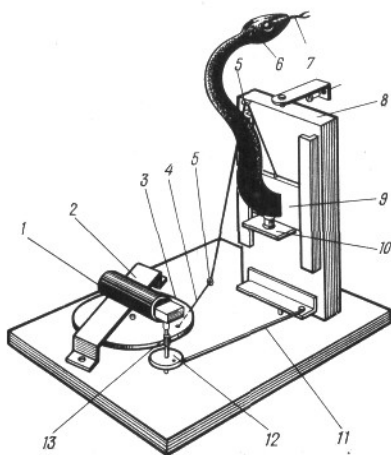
Конструкция механизма подъема и покачивания фигурки змеи
